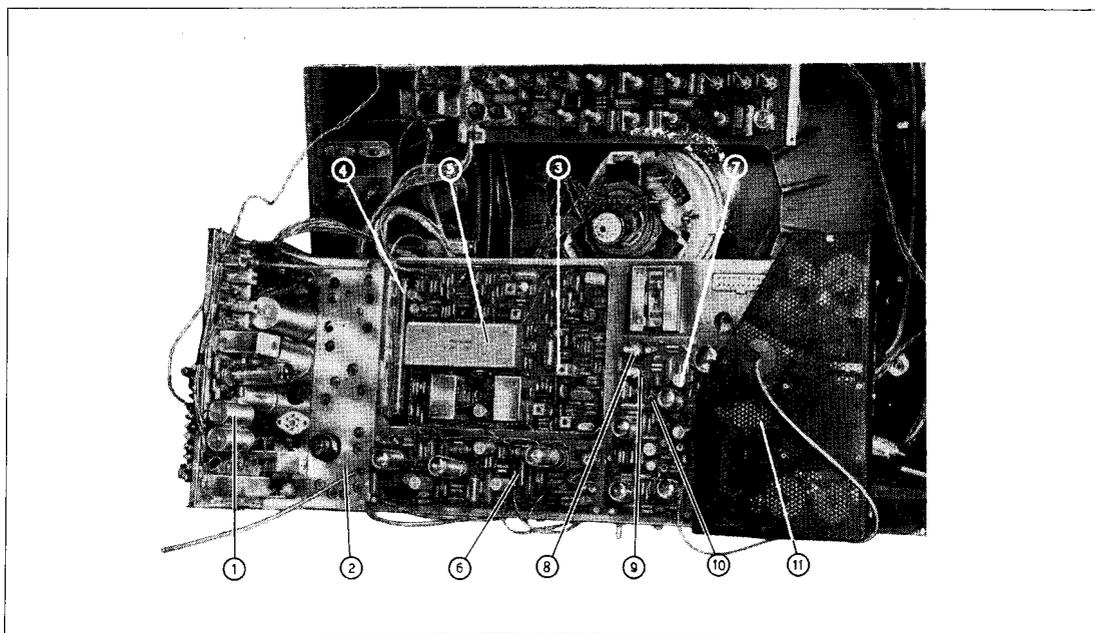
Vista dall'alto dell'assieme telaio GTV 8 C 125
